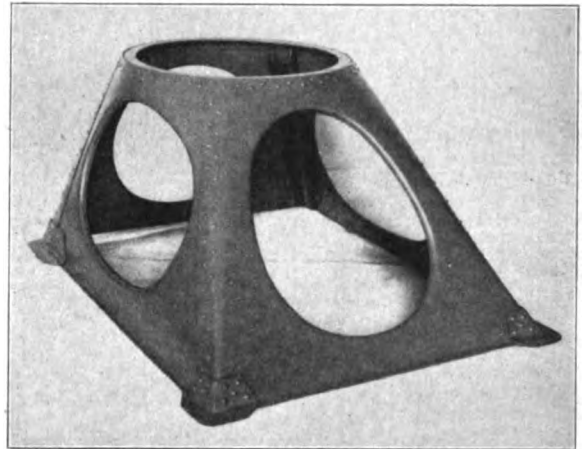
Motorbock in Elektronblech für ein Klemm-Sportflugzeug.
